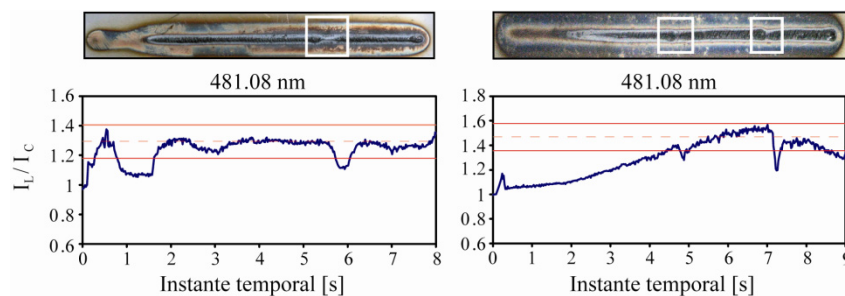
Detección de defectos de soldadura mediante SFFS y perfiles línea-continuo.
